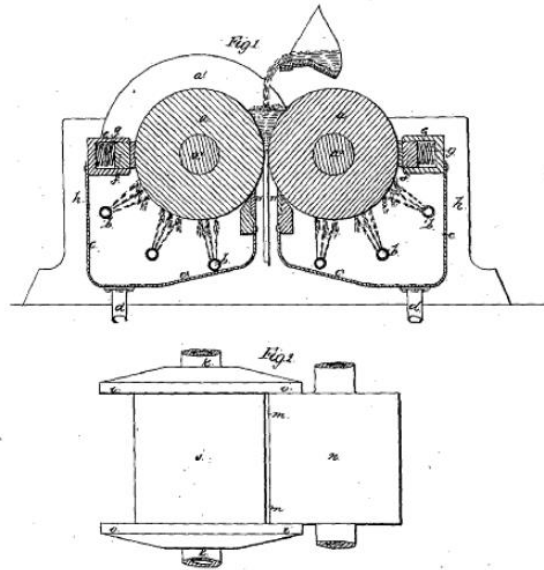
Зовнішній вигляд агрегату валкової розливки-прокатки, запатентований Генрі Бесемером
